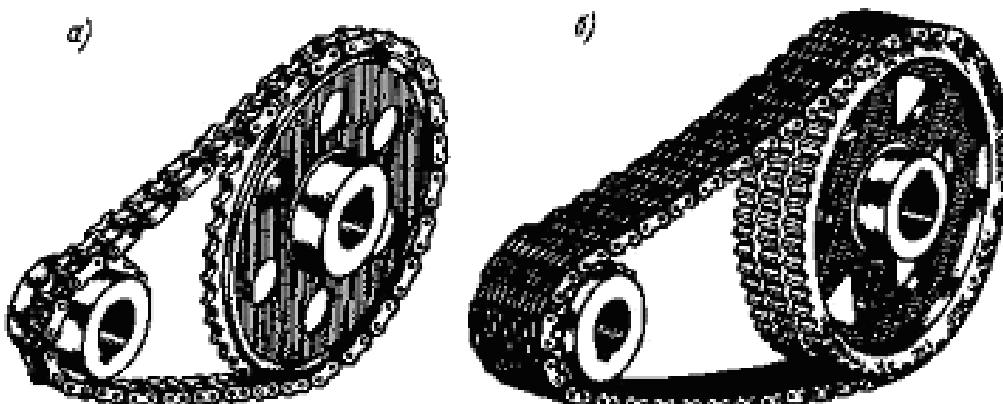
Цепная передача роликовой цепью а), зубчатой цепью б)
